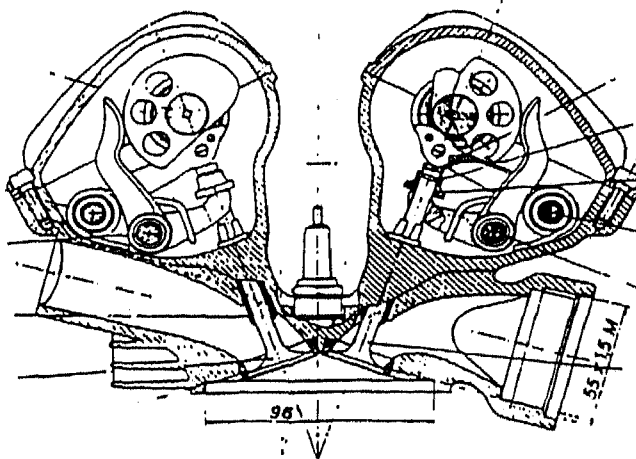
Seitenansicht/Querschnitt des Vierventiler 750 SS
